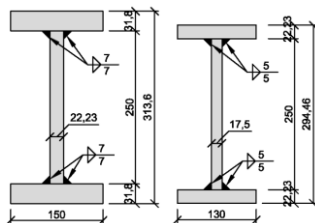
Querschnitte der geschweißten I-Profil [116]
